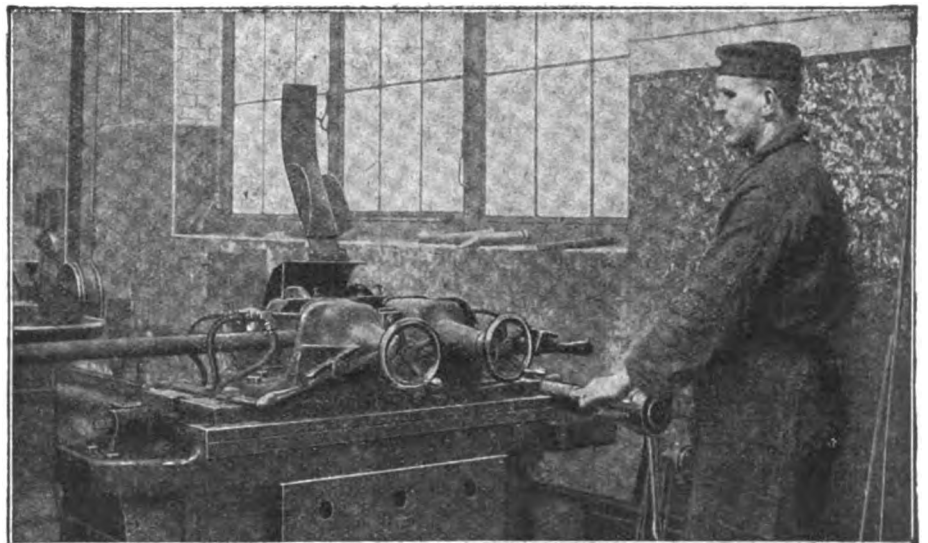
Elektrische Schweißmaschine für das Schweißen von Siede- und Rauchrohren in der Eisenbahnhauptwerkstatt Nied.
